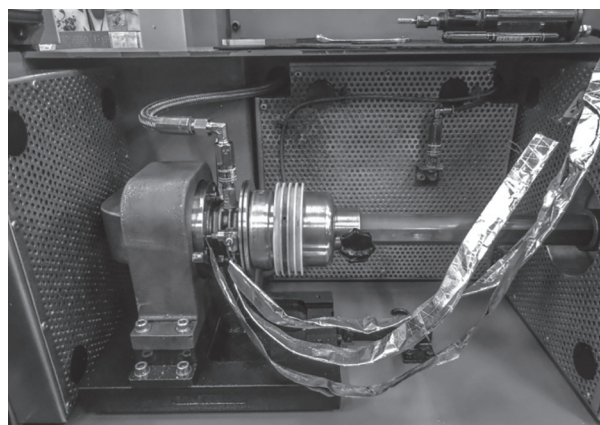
Картридж турбокомпрессора ТКР 50 с вибропреобразователем AP81 на балансировочном станке SCHENCK
